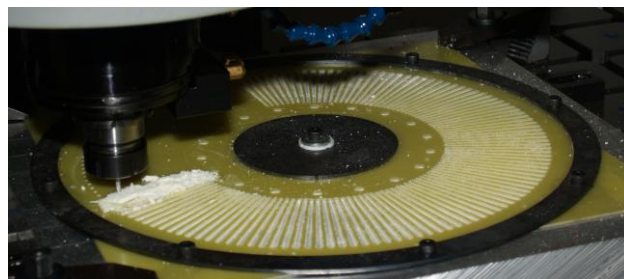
Обработка сборочного шаблона статора генератора на обрабатывающем центре
